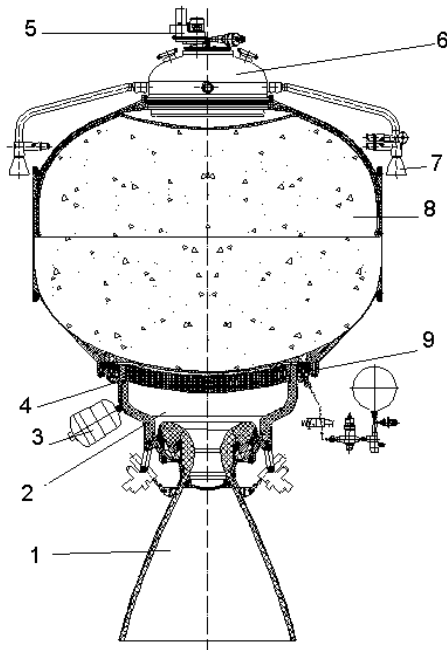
Маршевый ракетный двигатель на пастообразном топливе для верхних ступеней РН с механически регулируемым вектором тяги:
